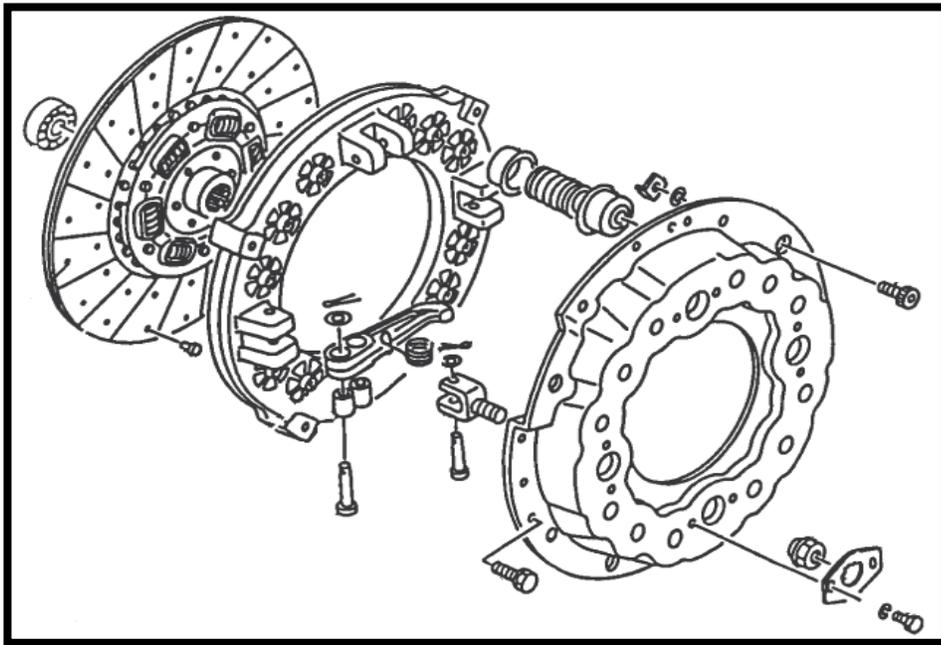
Embrague camión y tanquero: Fuente [31]
